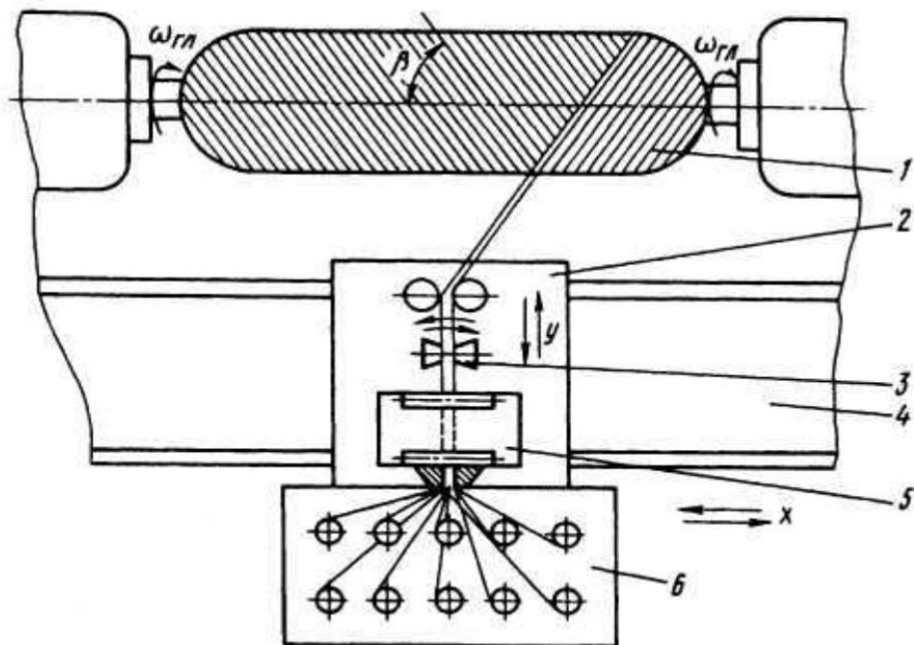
Кінематична схема координатного верстата для спіральної намотки
